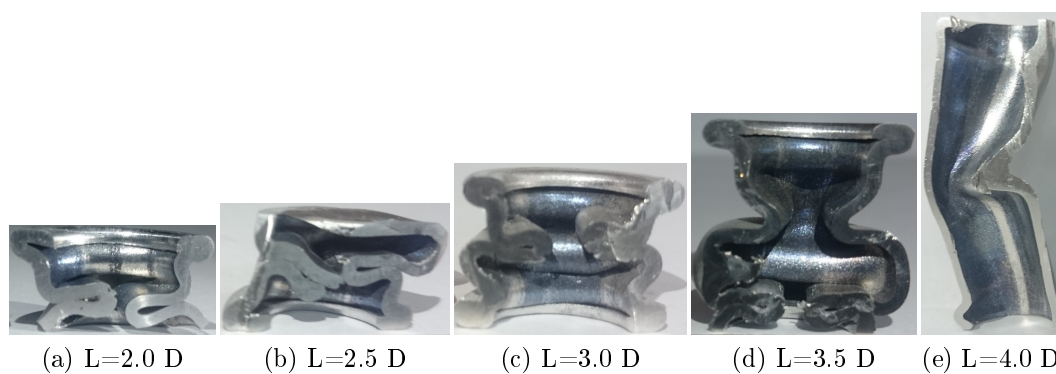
Vues des éprouvettes de compression déformées après coupe axiale .
